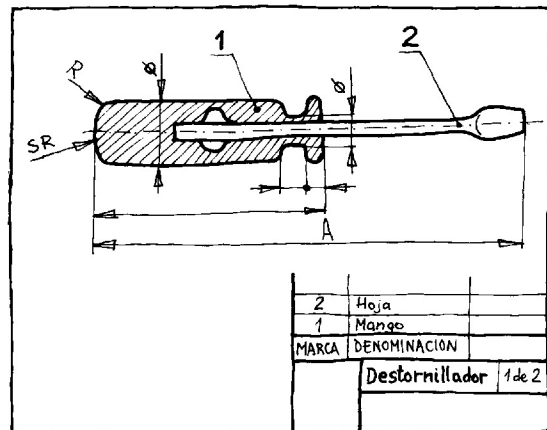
Dibujo de conjunto de un destornillador con unión por elemento aglutinador
